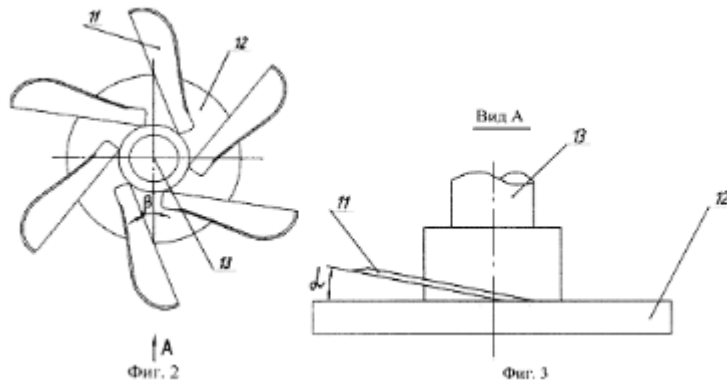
Рабочий орган фронтального лесопожарного грунтомета
